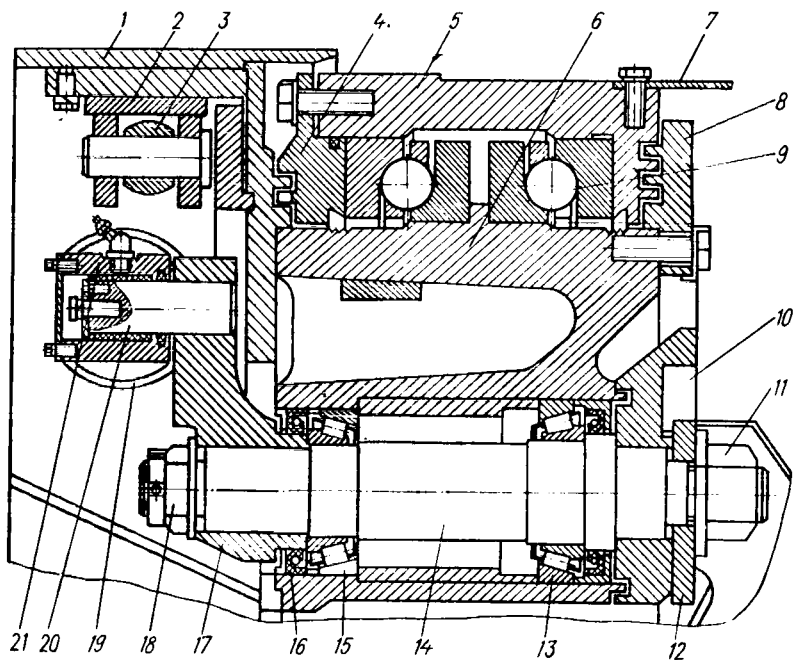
Окорочная головка станка 20К63-1:
